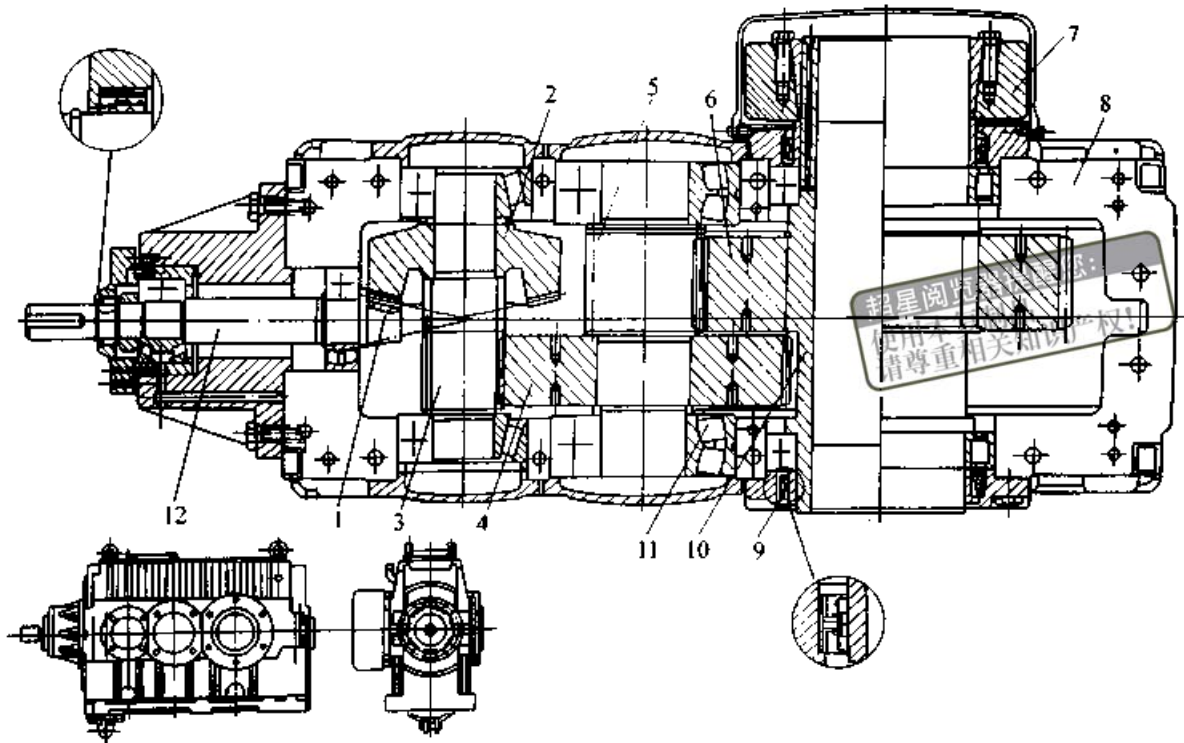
M3RHT70—90 锥齿轮—斜齿轮减速器
